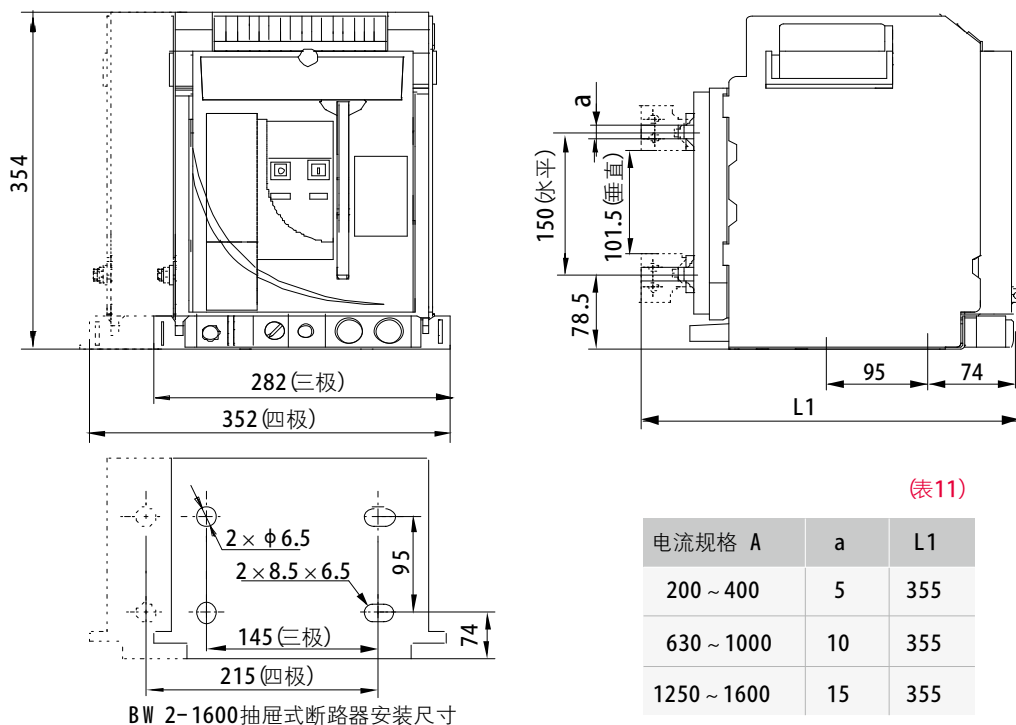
BW2-1600 抽屉式断路器外形及安装尺寸
